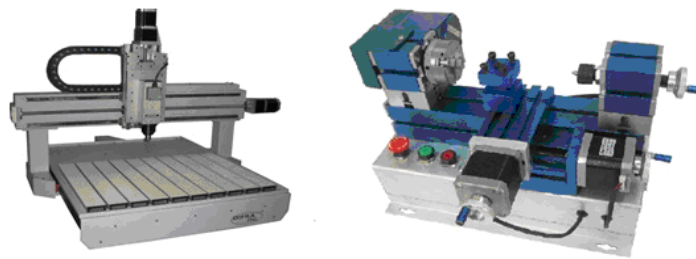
Izquierda Fresadora CNC, Derecha Torno CNC
